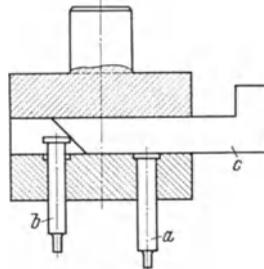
Werkzeug zum Werkstück Abb. 105.
